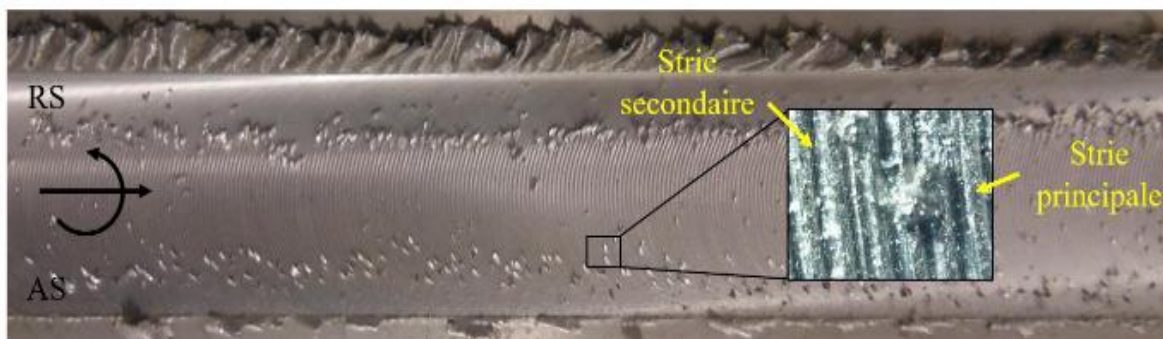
Détails de la rugosité de surface d'une soudure en 6061-T6 [14]
